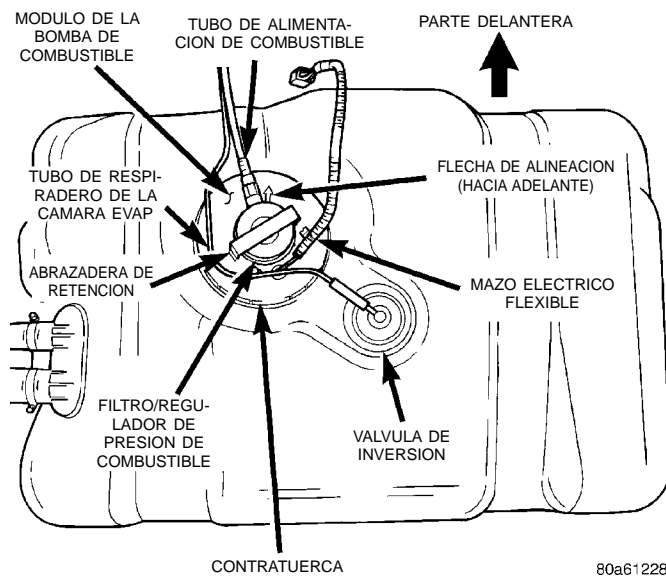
Vista superior del depósito y el módulo de la bomba de combustible
